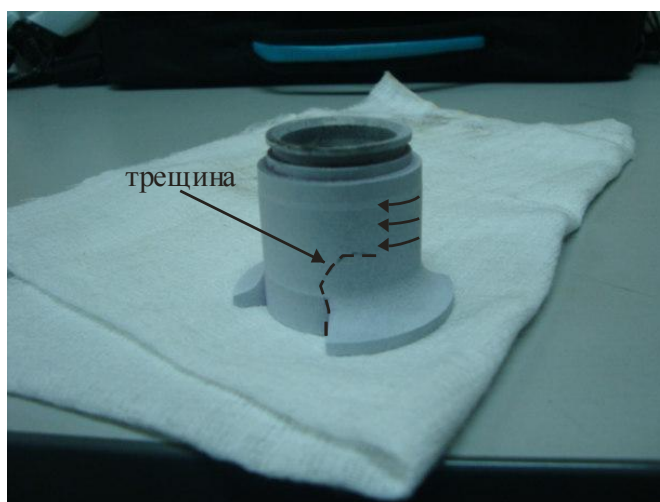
Общий вид рестриктора с поверхностной трещиной.
